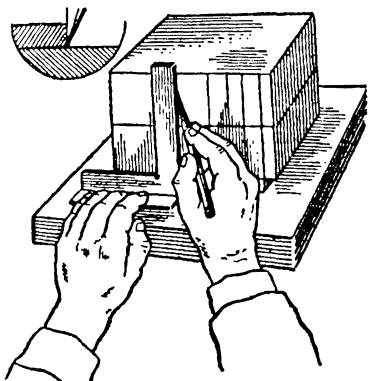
Разметка вертикальных линий с помощью угольника
